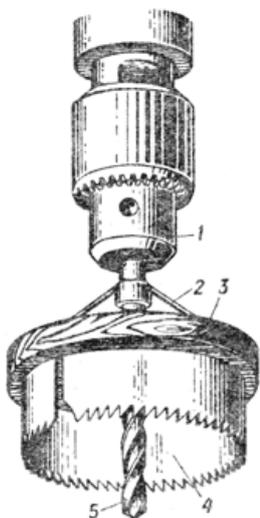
Приспособление для сверления отверстий большого диаметра: 1 – патрон дрели; 2 – металлические тяги; 3 – сверло; 4 – направляющая; 5 – режущая кромка.
